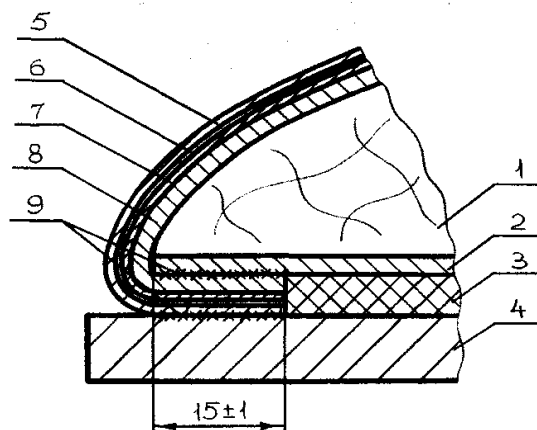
Схемы швов, соединяющих детали верха обуви
